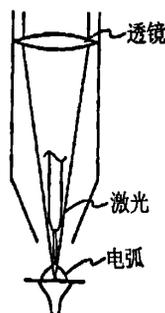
同轴 TIG/MIG-YAG 焊接示意图
